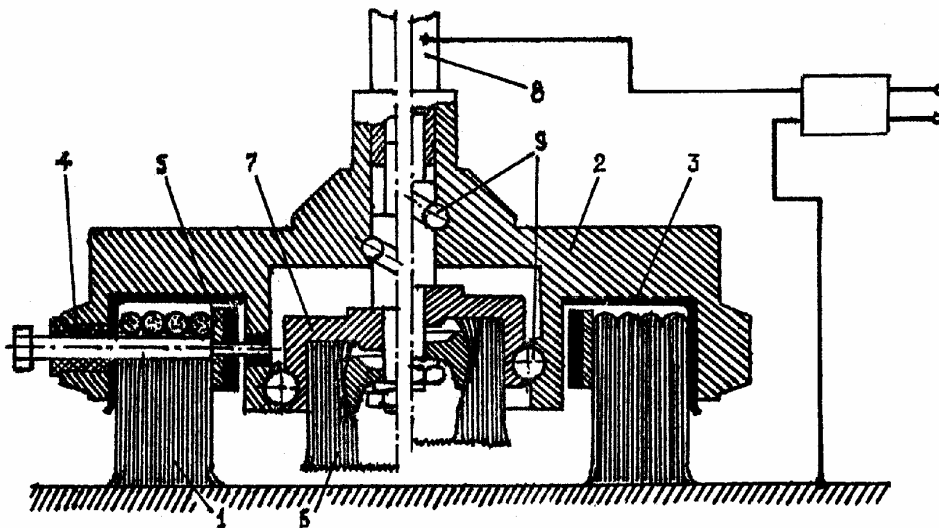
Торцева щітка для поверхневого ТМО листового прокату
